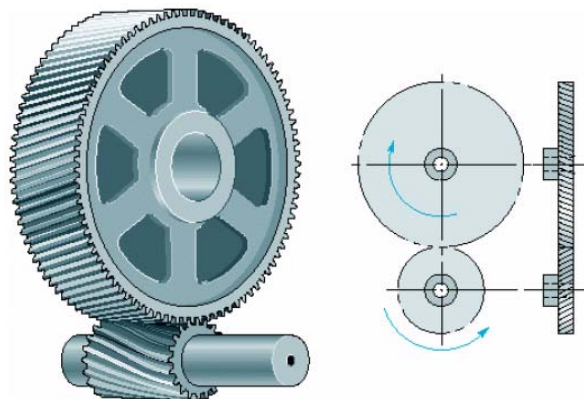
Engrenagens cilíndricas de Dentes rectos [5]
